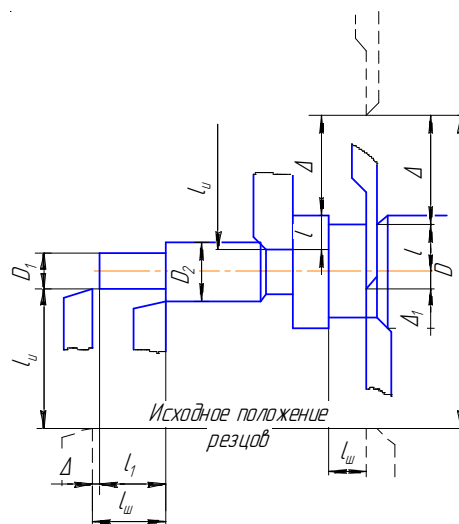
Рабочий ход инструмента при обработке деталей
